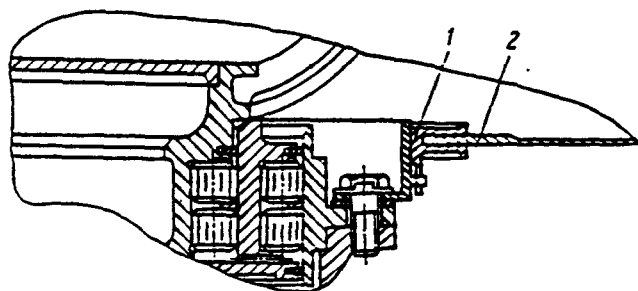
Соединение заднего уплотнения реверсивного устройства с узлом опоры створки:
